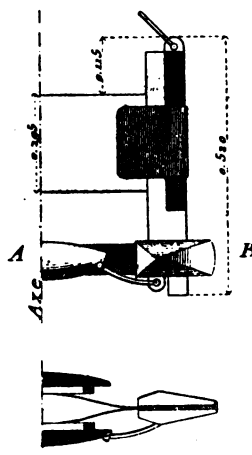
Appareil pour la prise de courant. Demi-plan et demi-élévation.
